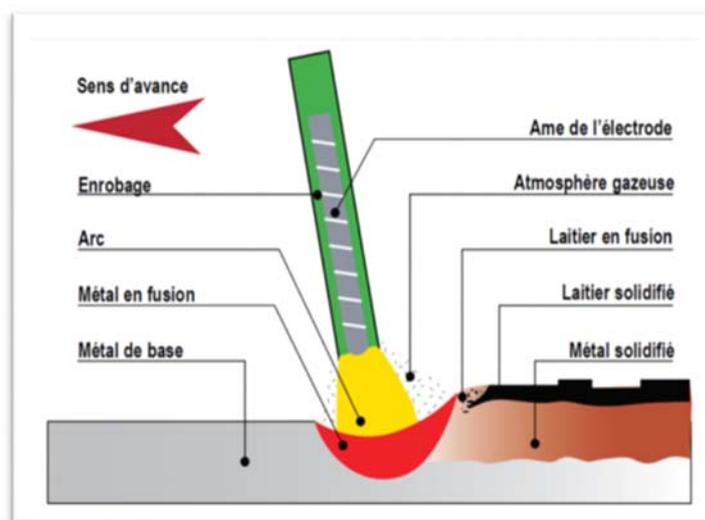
Soudage à l'arc électrique enrobée.
